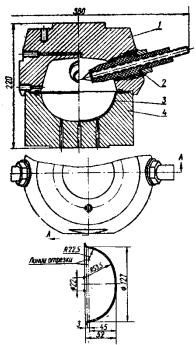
Оснастка для электрогидравлической штамповки деталей из плоской заготовоки: 1 – рабочая камера; 2 – електрод; 3 – заготовка; 4 – матрица
